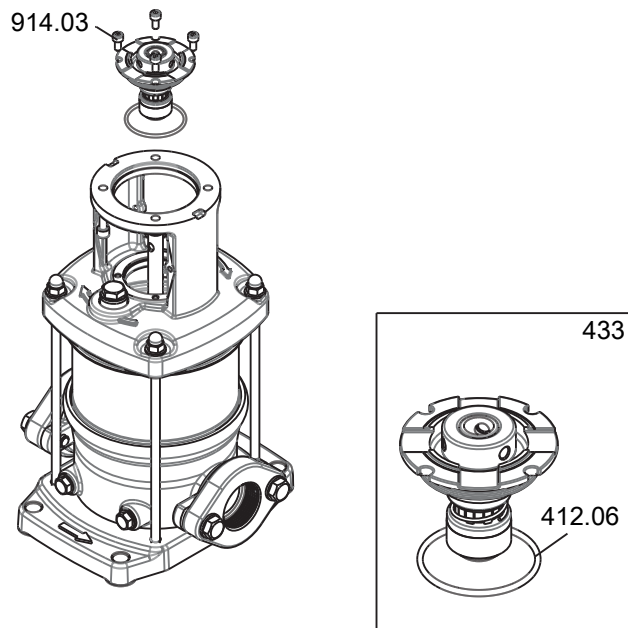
Gleitringdichtung ausbauen (Beispielzeichnung)
